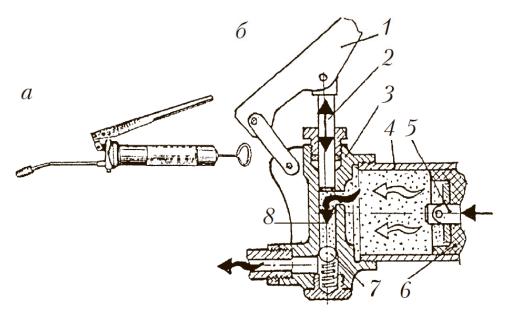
Ручной рычажный нагнетатель смазки:
